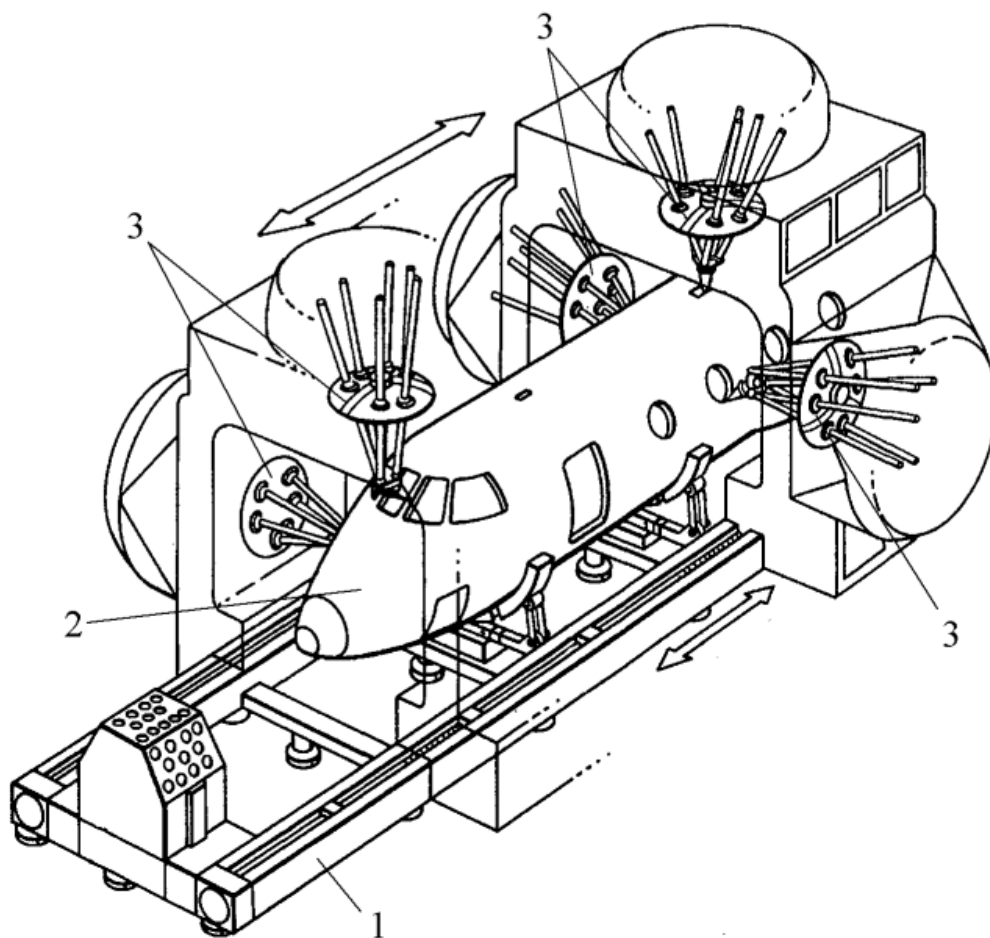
Технологічне обладнання для фрезерування отворів у корпусі аерокосмічного апарату
